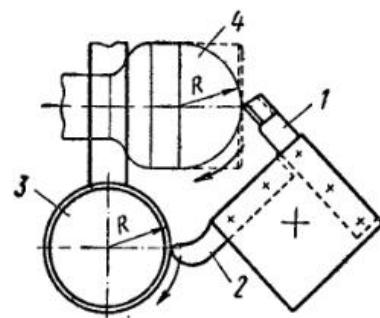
Приспособление на суппорте для обработки сферических поверхностей:
